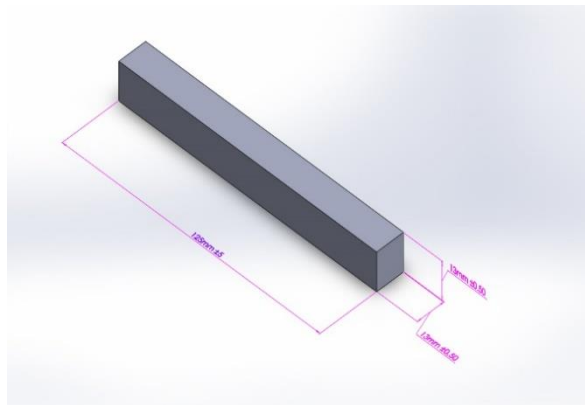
Molde hecho en Solidworks de la probeta para prueba de inflamabilidad.
